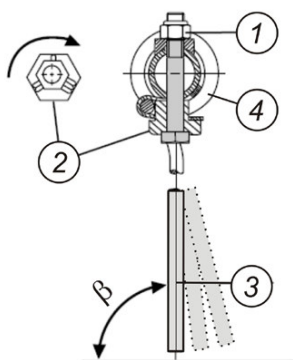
Схема к настройке вертикального положения зубьев ротора: 1 – крепежная гайка; 2 – эксцентриковая втулка; 3 – зуб; 4 – труба ротора
